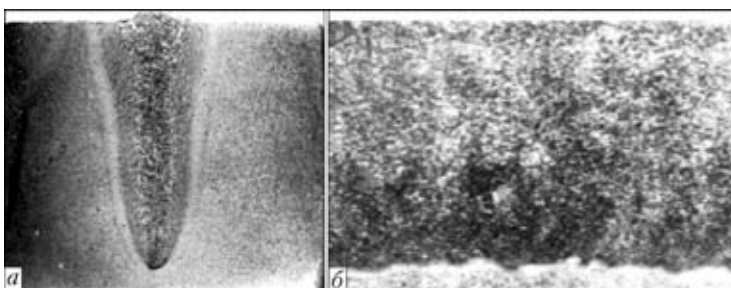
Макроструктуры ($\times 1$) сварного шва, полученные в поперечном (а) и продольном (б) сечениях при сварке с Х-образными колебаниями
